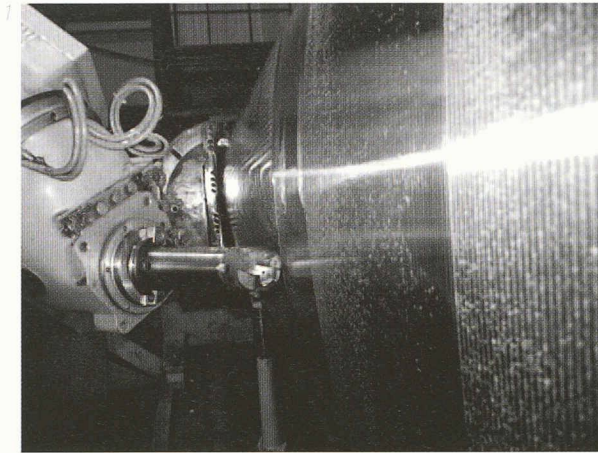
Usinage du voile de quille sur un centre 6-axes
